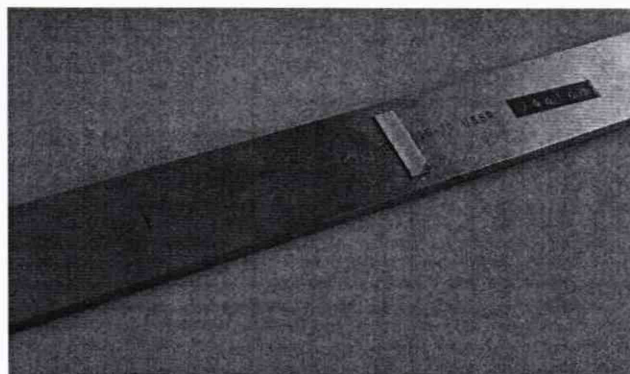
Установка концевой меры на рабочую поверхность линейки поверочной
